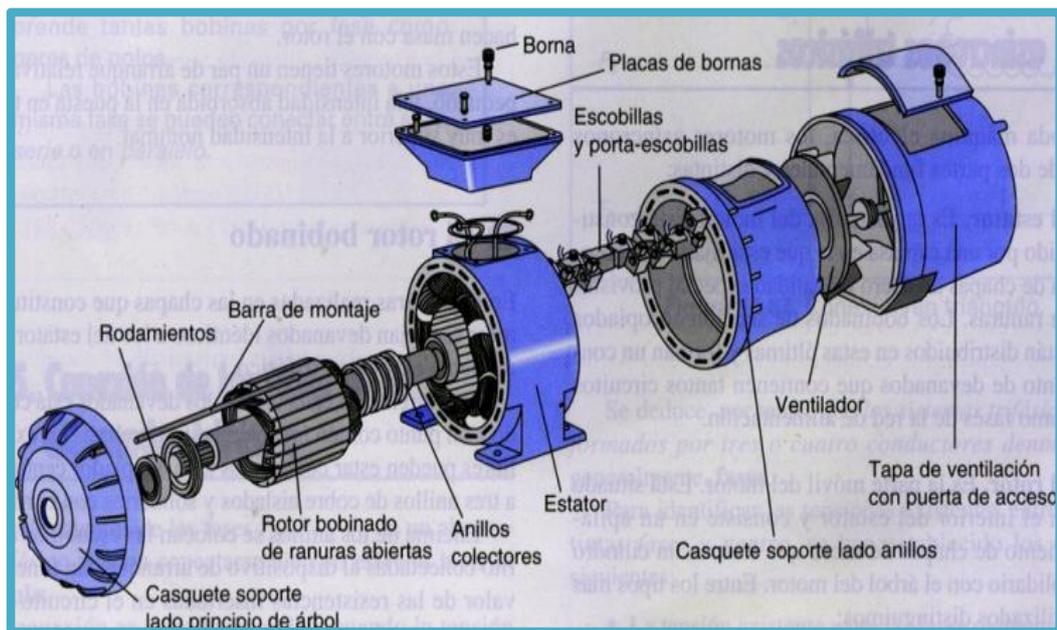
PARTES DEL MOTOR DE ROTOR DE ANILLOS ROZANTES
